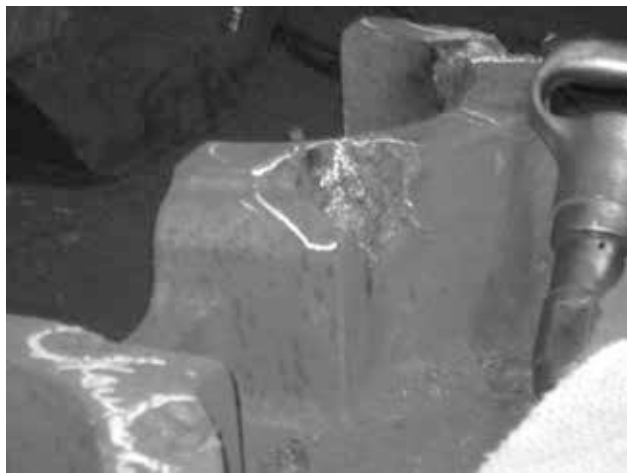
Фасонная отливка готова к ремонтной сварке
